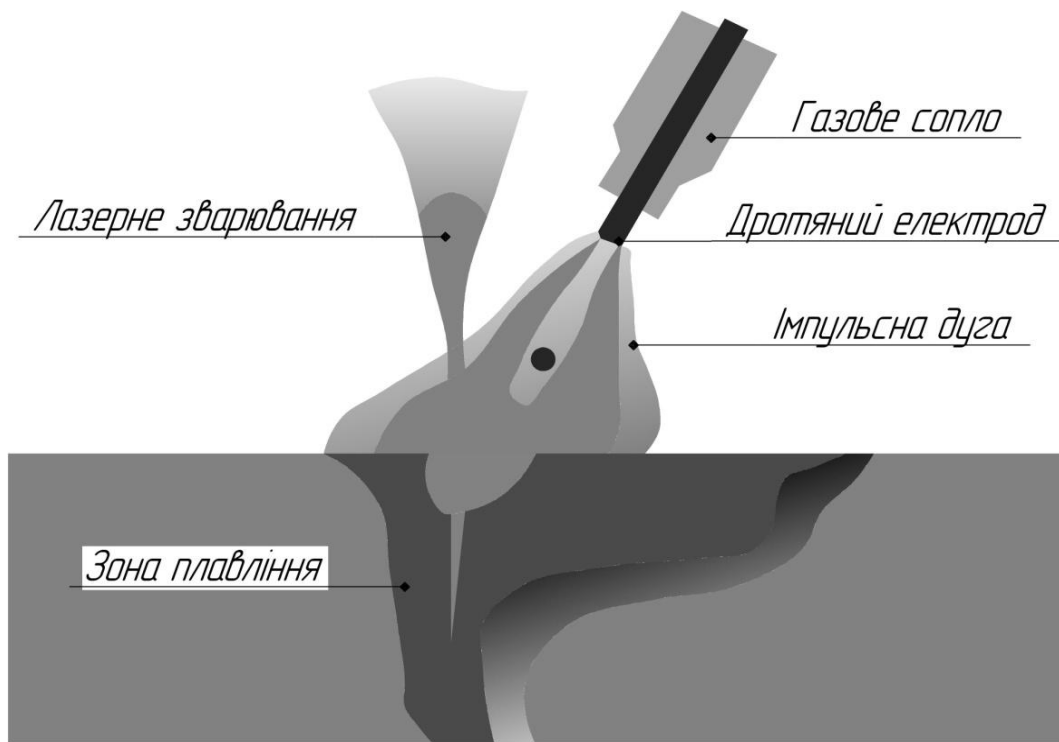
Схема гібридного лазерно-дугового зварювання
